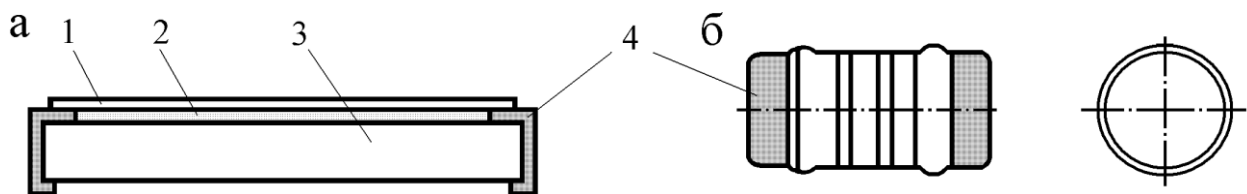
Корпуса пассивных элементов для поверхностного монтажа:
